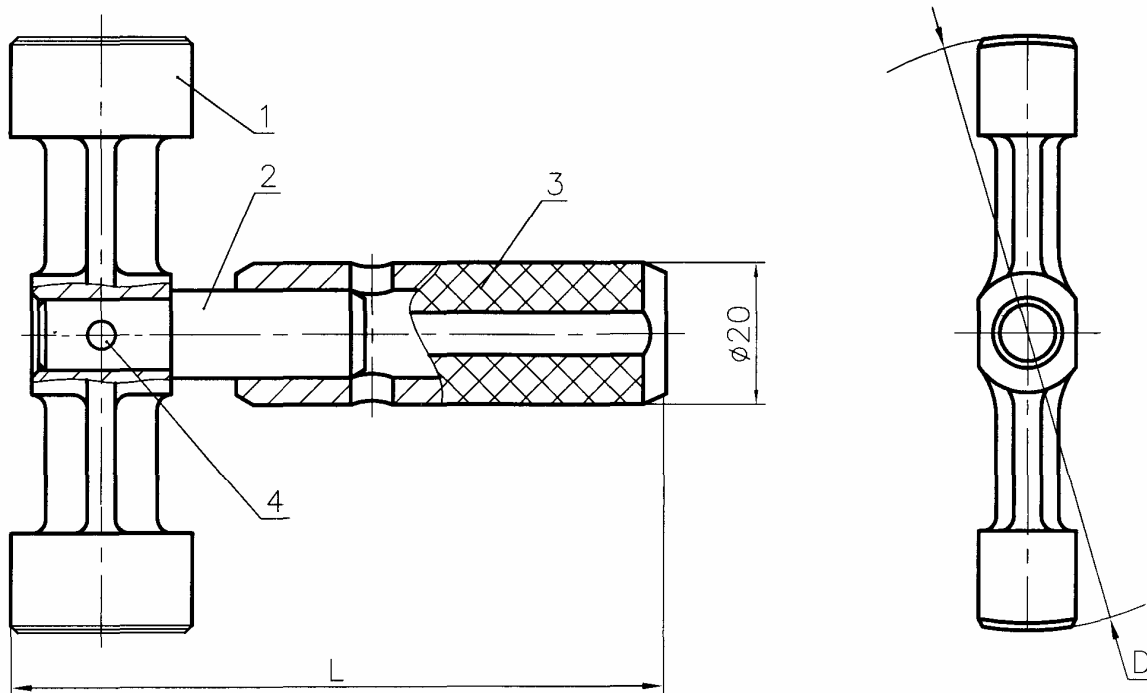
Гладкий штампованный неполный калибр-пробка:
